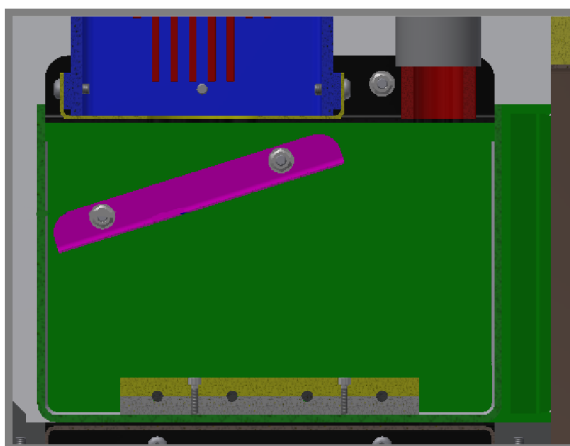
Detail uložení Peltierova článku a pasivního chladiče
